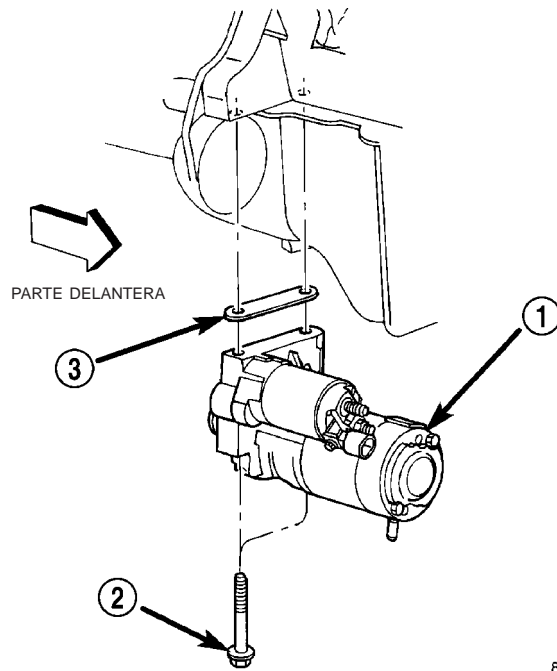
Desmontaje e instalación del motor de arranque - Motor 2.5L
